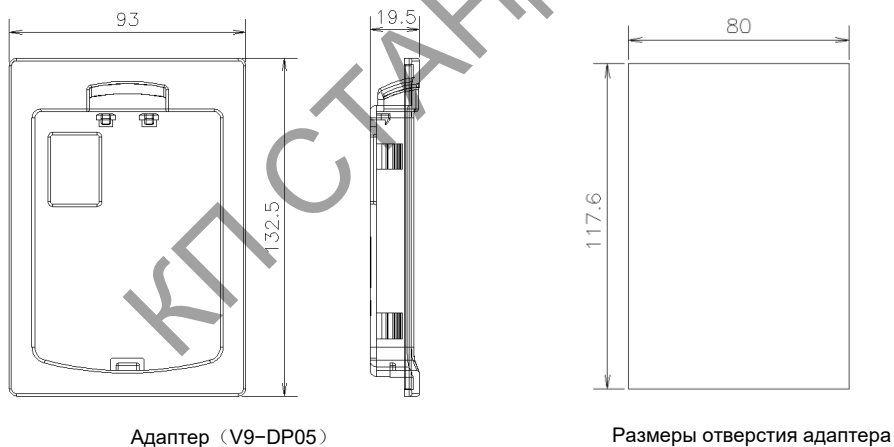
Внешний вид адаптера и монтажные размеры
